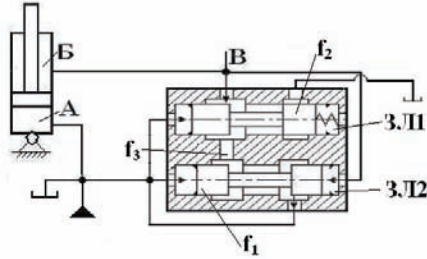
Автоматичний регулятор швидкості: А – поршнева порожнина; Б – підпоршнева порожнина; ЗЛ1, ЗЛ2 – золотники АРШ; f_1, f_2, f_3 – площі каналів АРШ
